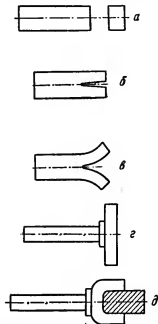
Эскизы переходов при ковке вилки шарнирной передачи сенокосилки:
